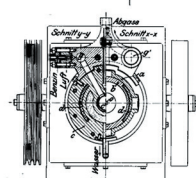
Батарейный двигатель конструкции Б. Г. Луцкого
